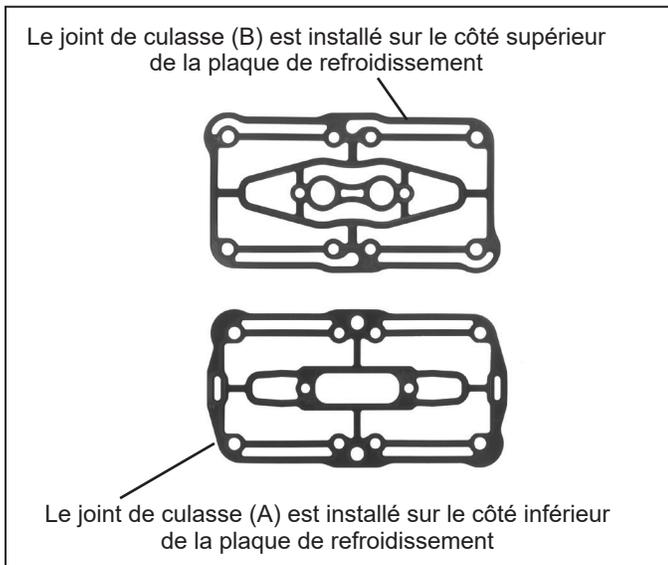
Position des joints de tête pour compresseur Bendix® 720cc
